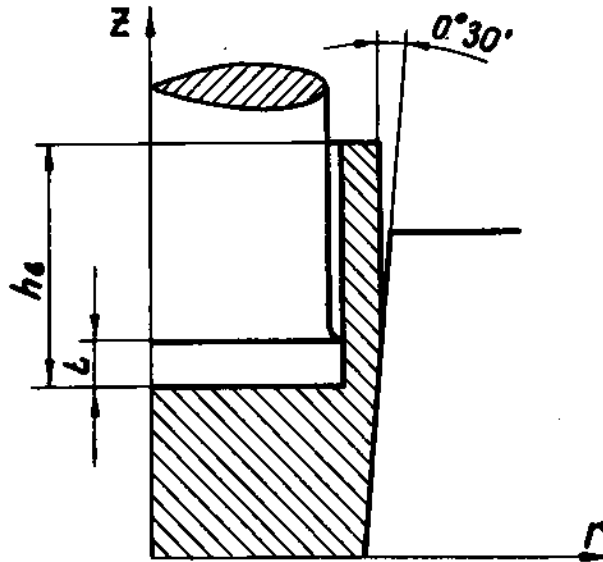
Схема зворотного видавлювання в конічній матриці.
